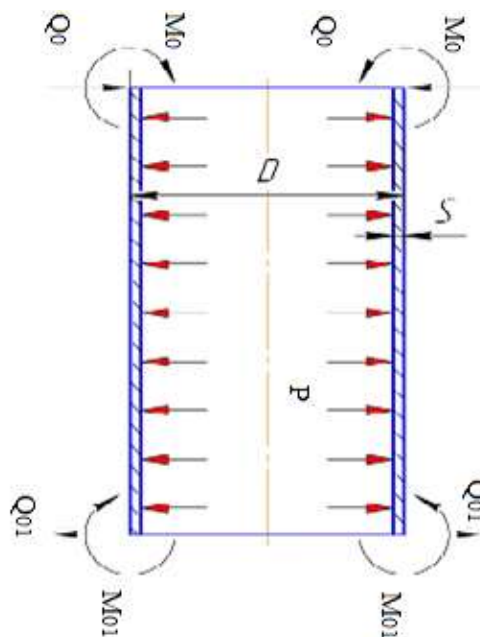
5 – Розрахункова схема циліндричної обичайки
